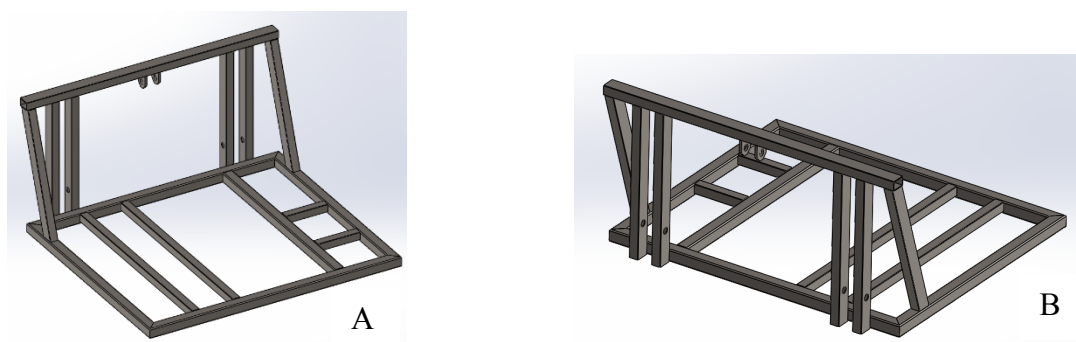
(A) Vista isométrica traseira do chassi e (B) vista isométrica frontal do chassi.
